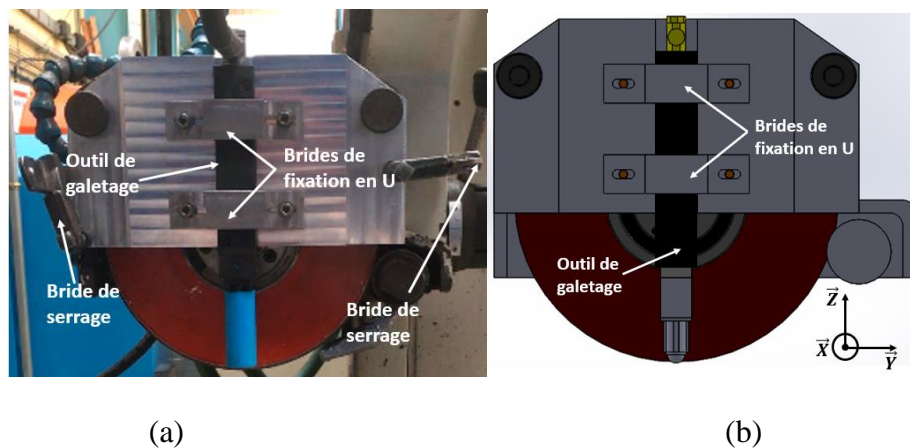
(a) Fixation de l'outil de galetage sur la plaque en aluminium, (b) CAO des brides de fixation en U.
